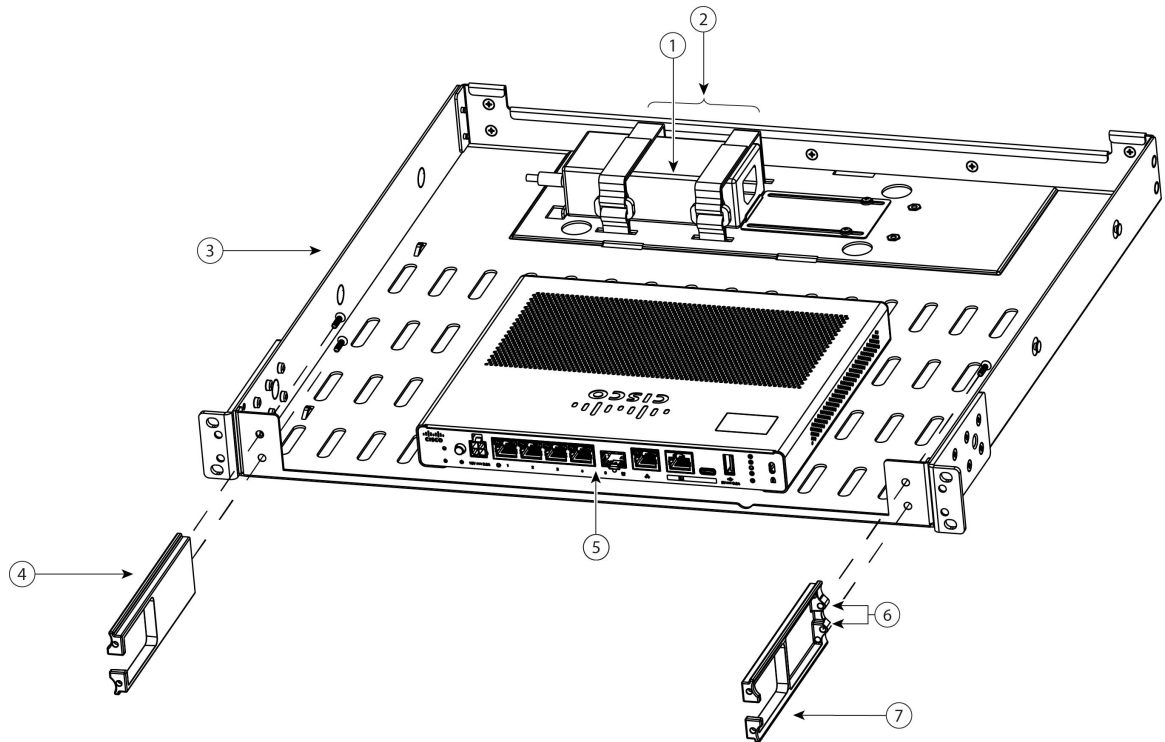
Installez le châssis sur l'étagère de montage en rack
